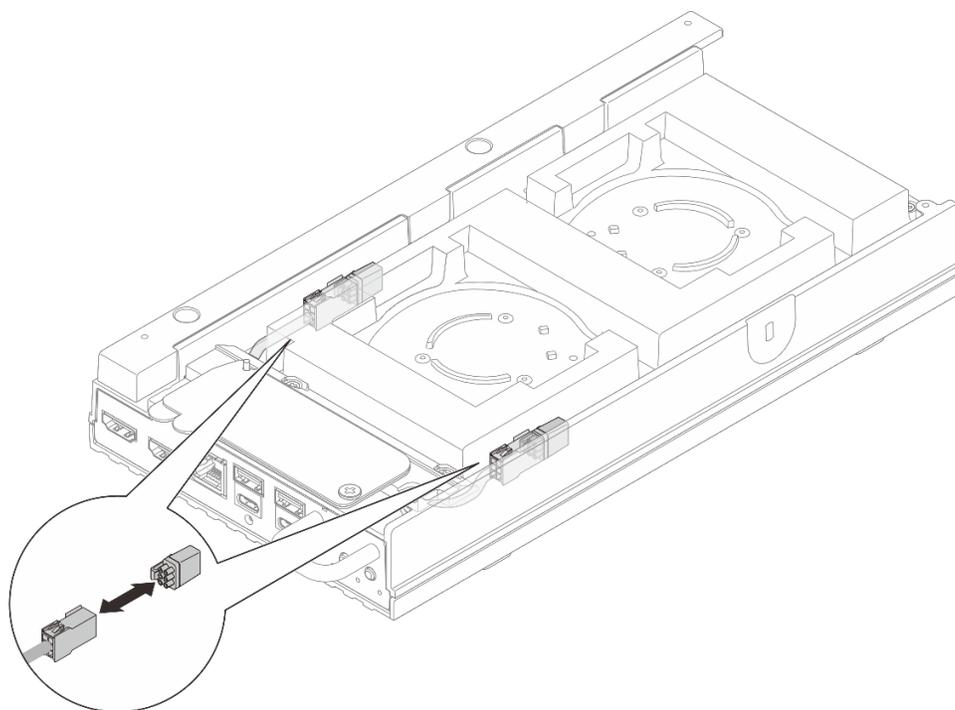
Rimozione dell'elemento di riempimento antipolvere dal cavo del bridge della ventola
